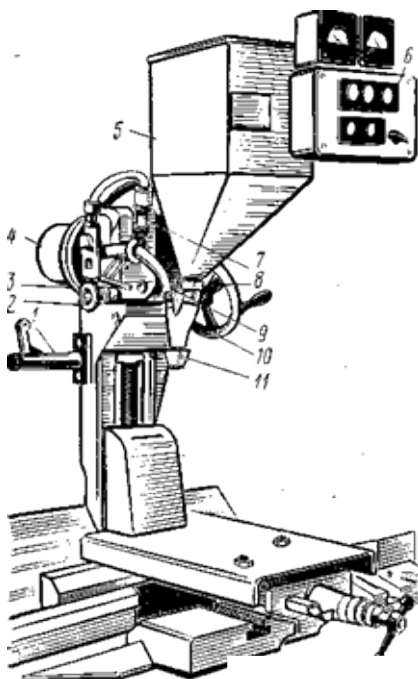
Автомат А-409 для наплавки цилиндрических деталей под слоем флюса [17]
